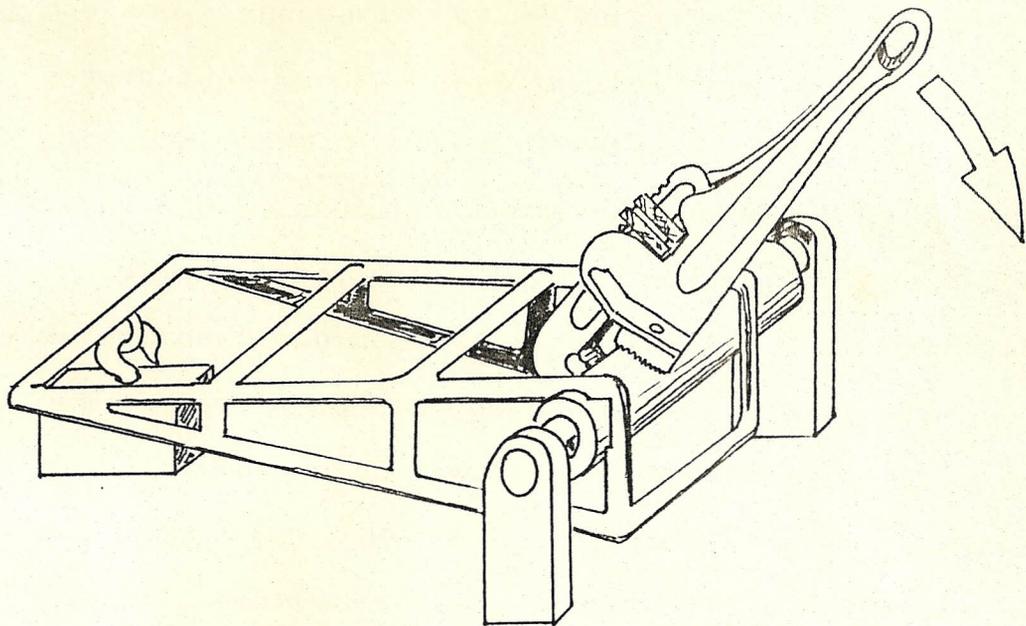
ENSAYO DE DOBLADO DEL CONJUNTO ENSAMBLADO
